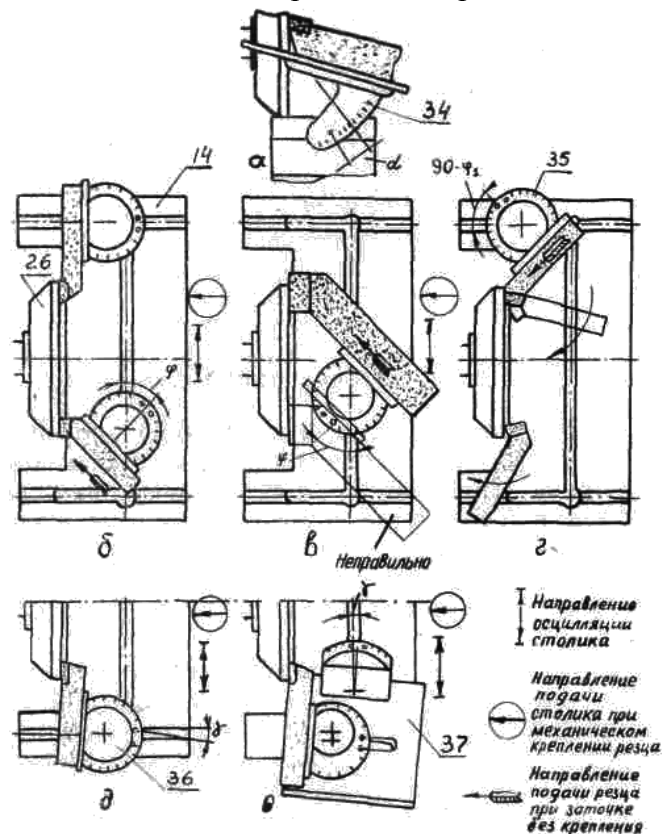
Схемы заточки резцов на алмазно-заточном станке.
